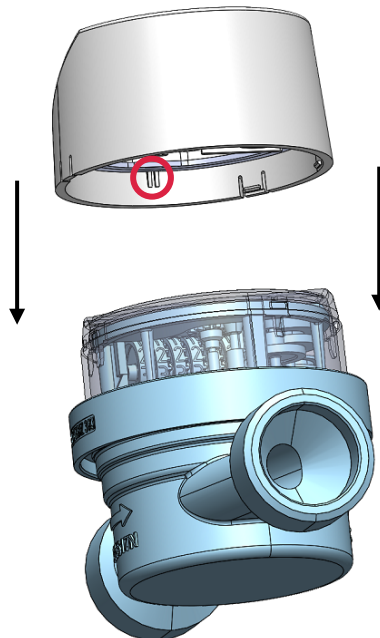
Ansicht des Wasserzähleraufsatzes OP-O4-1b, vor der Montage auf dem Wasserzähler JS Smart +.
